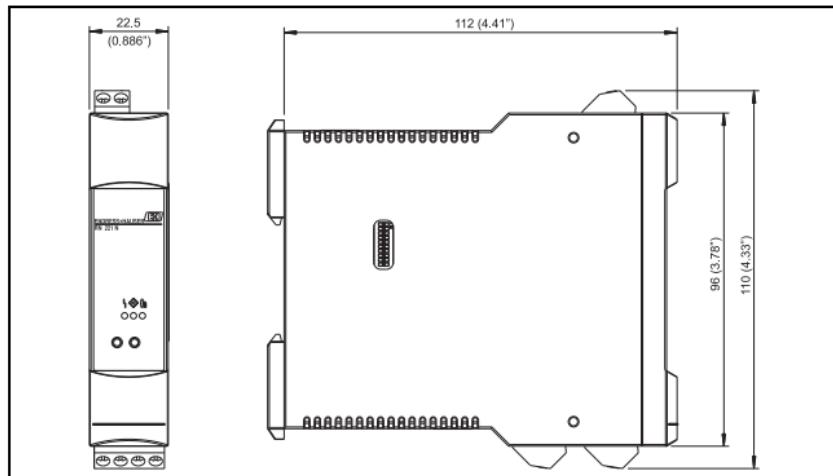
Dimensiones en mm (dimensiones en pulgadas indicadas entre paréntesis)
